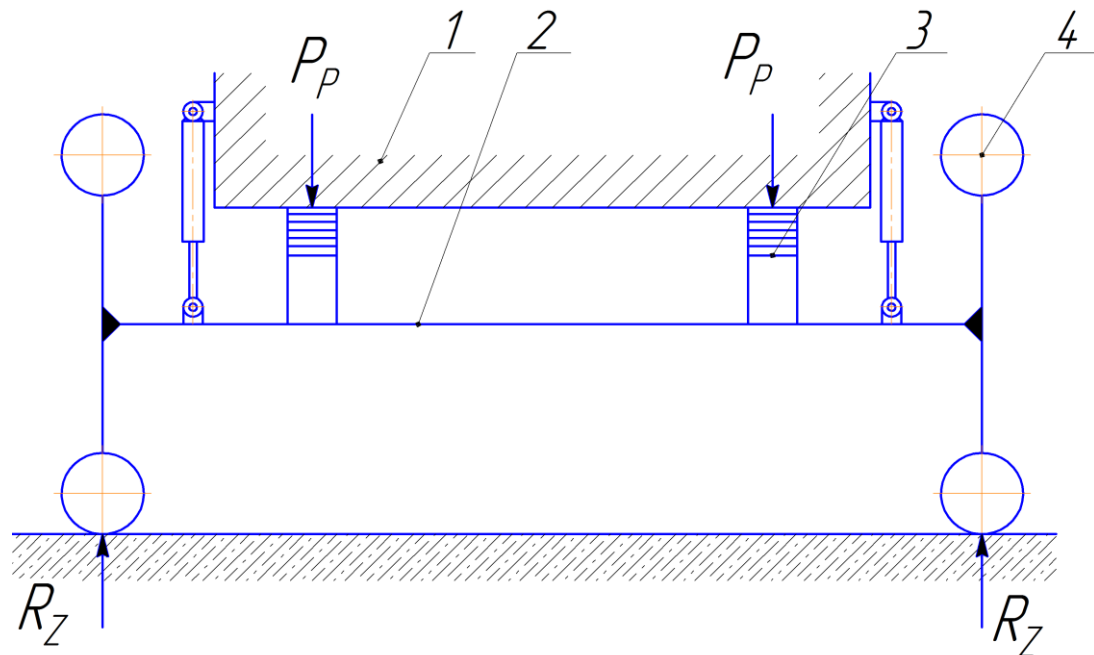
Кинематическая схема разрабатываемой передней подвески
